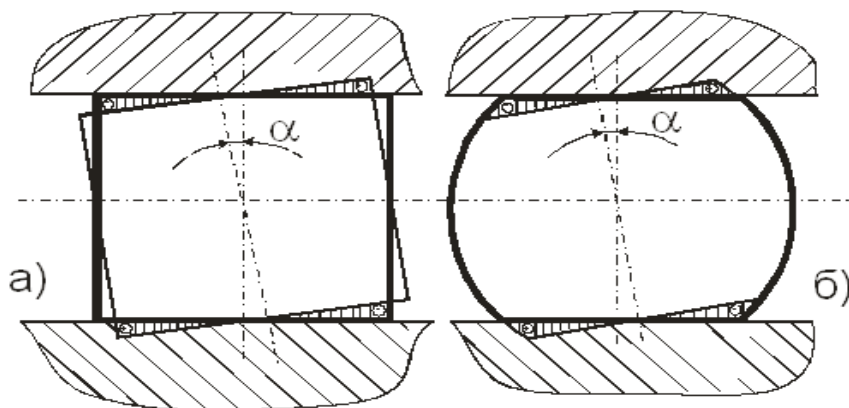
Разворот пружинного вкладыша различного сечения, исполнения (а и б), при его торцовом сжатии в подшипнике
